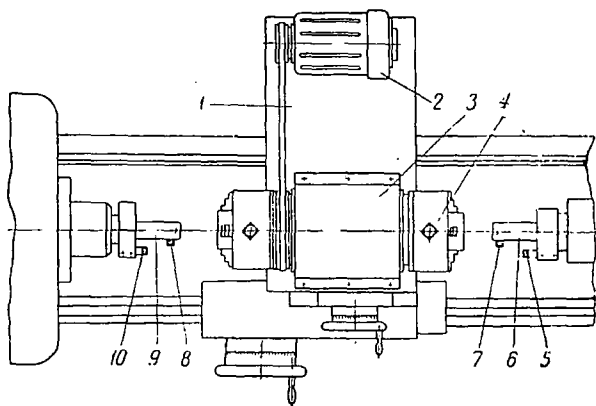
Приспособление для точной расточки труб с двух концов за одну установку.
